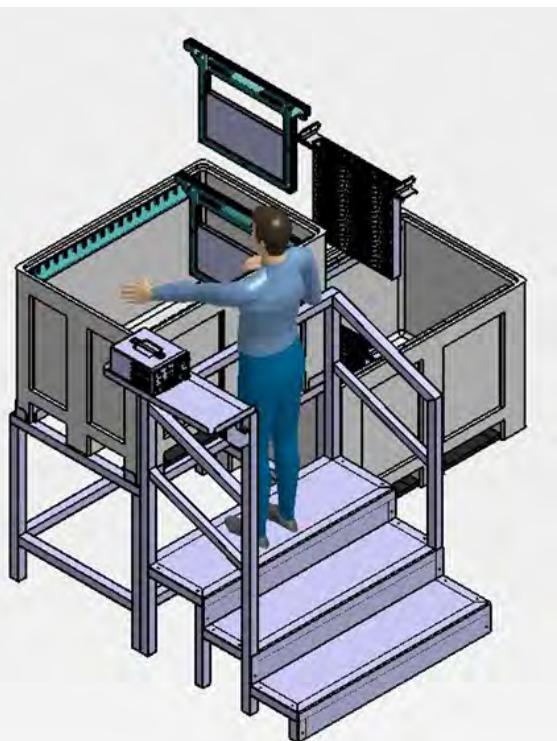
Dalla sperimentazione in laboratorio alla progettazione dell'impianto scala reale
